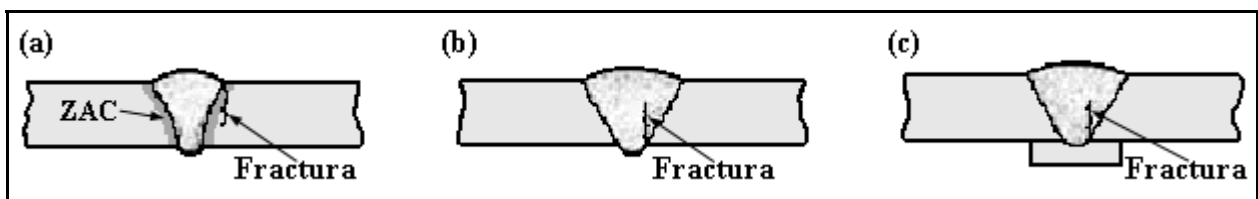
Fracturas en especímenes con soldadura a tope. (a) Entre el metal base y la ZAC, iniciando en la punta de la soldadura, (b) y (c) en la soldadura, iniciando en la raíz y respaldo.
